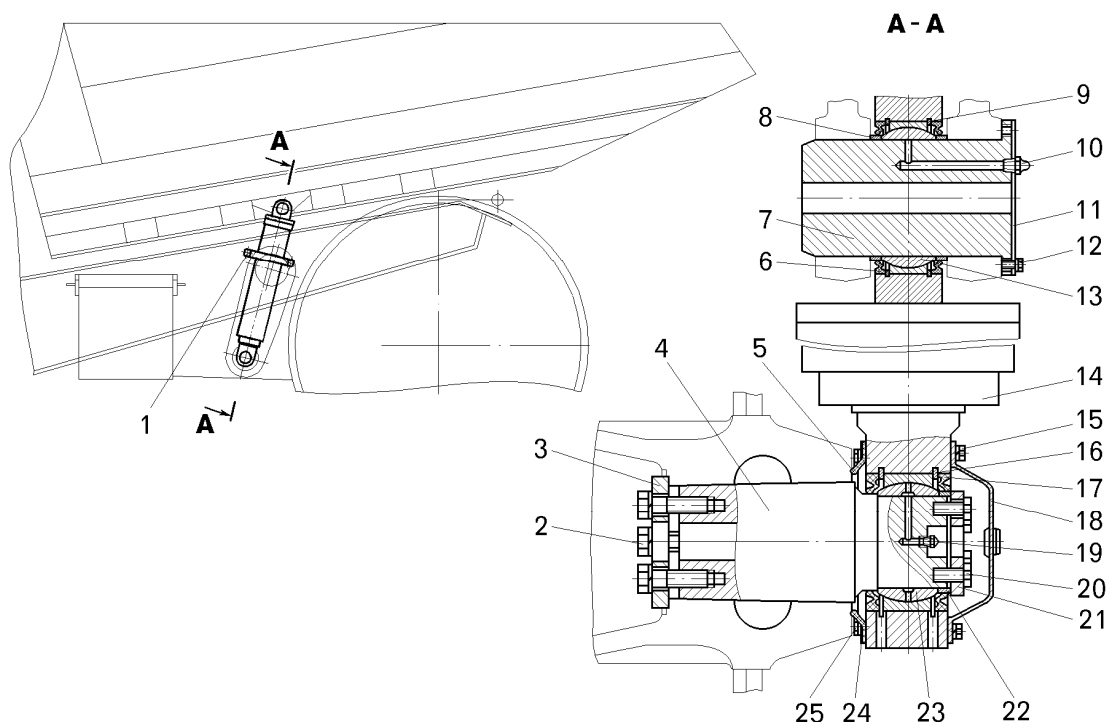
Установка цилиндров опрокидывающего механизма:
